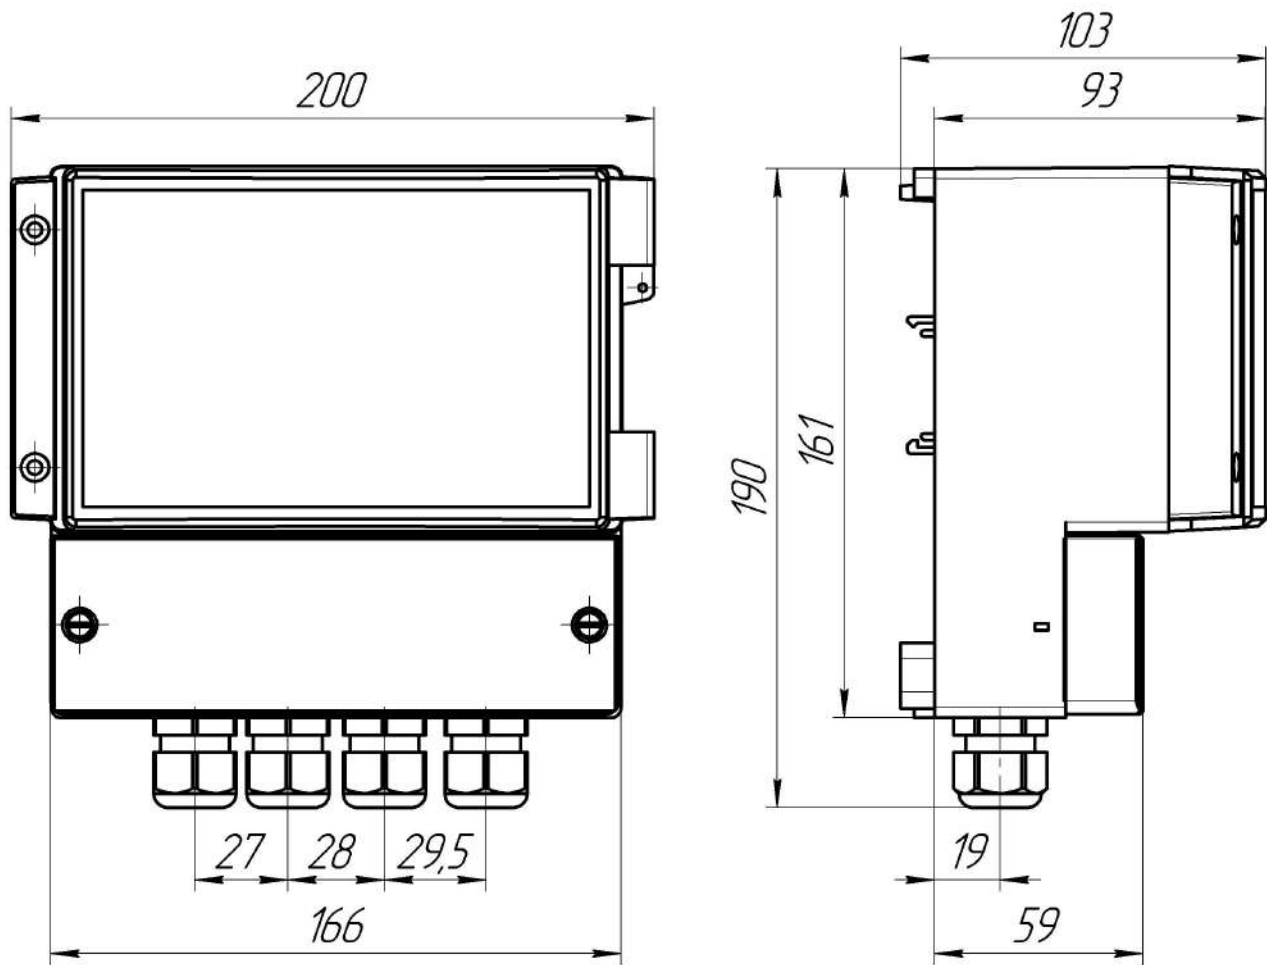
Габаритные размеры корпуса настенного ионтажа
